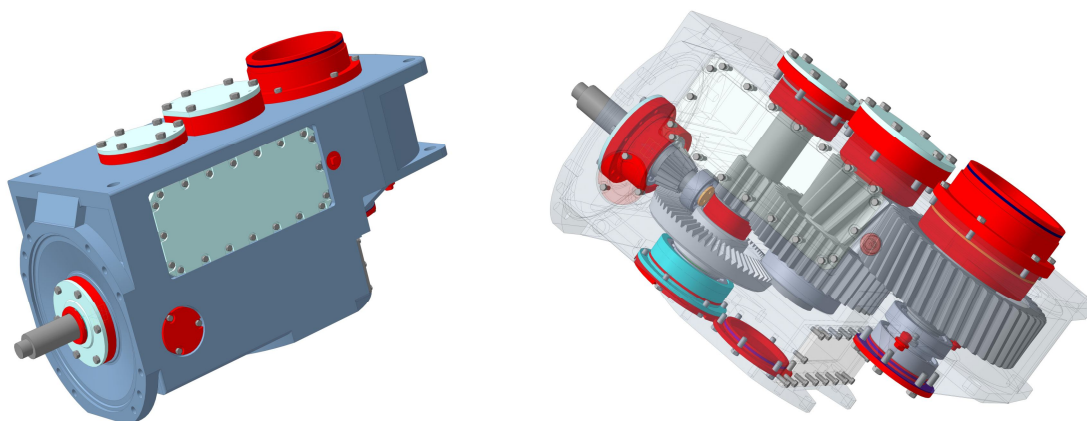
Твердотельная модель коническо-цилиндрического редуктора концевой приводной станции
